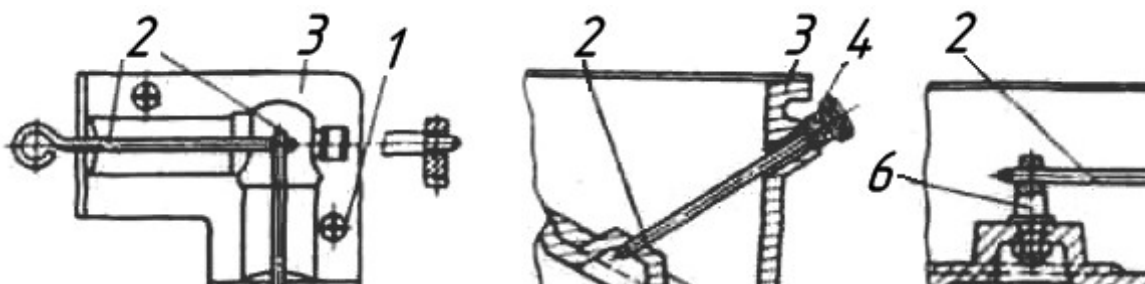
Схема установки душников в металлических стержневых ящиках: 1 – штырь; 2 – душник; 3 – стержневой ящик; 4 – гайка; 5 – ручка; 6 – подставка
